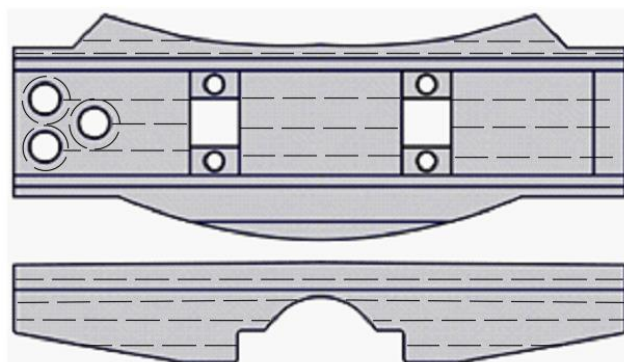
Схема сканирования тормозного башмака клещевого механизма
